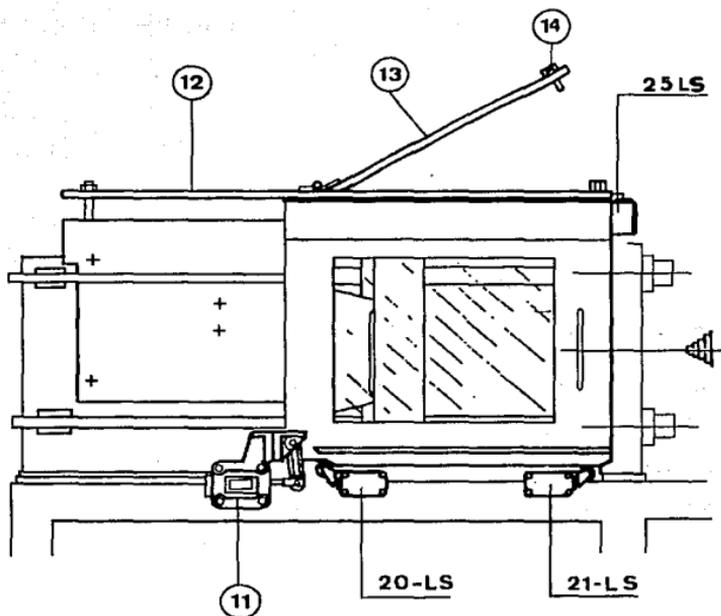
VISTA FRONTAL NEGRI BOSSI.
